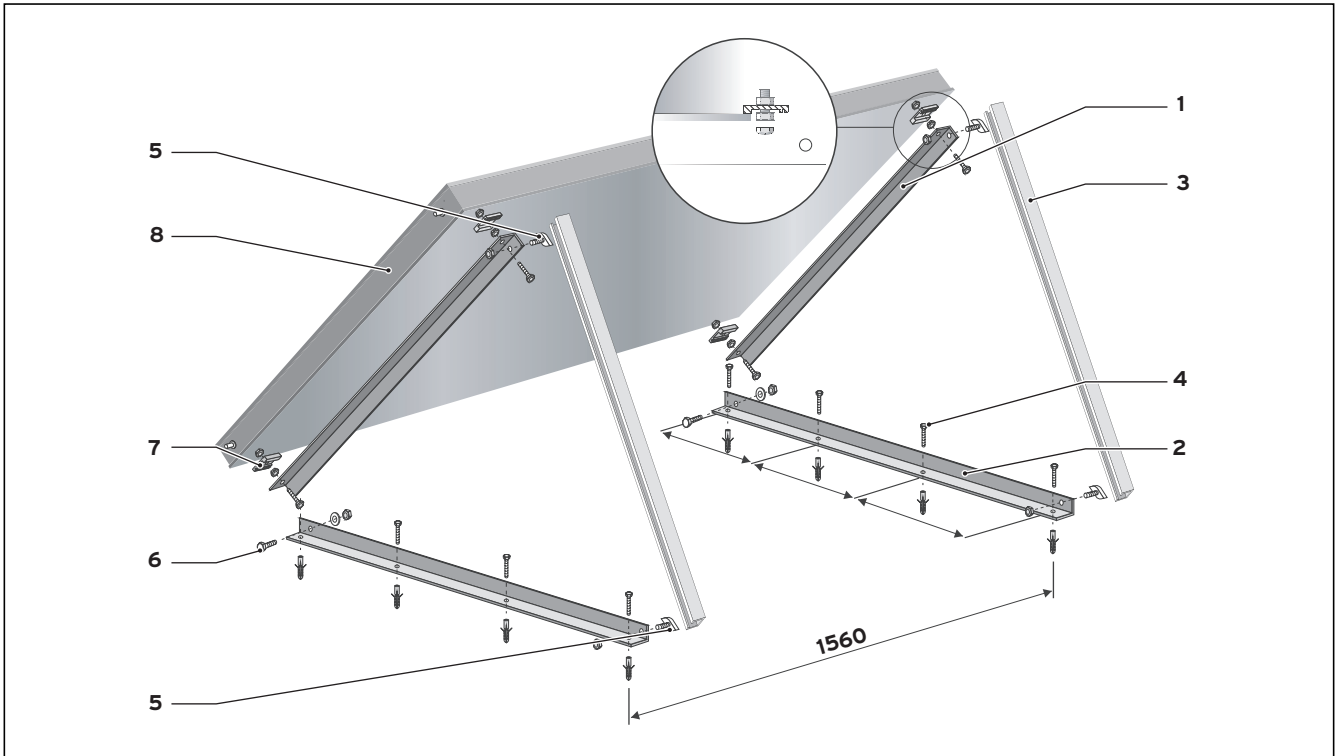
Module pour montage sur toit plat et pour montage horizontal des capteurs
